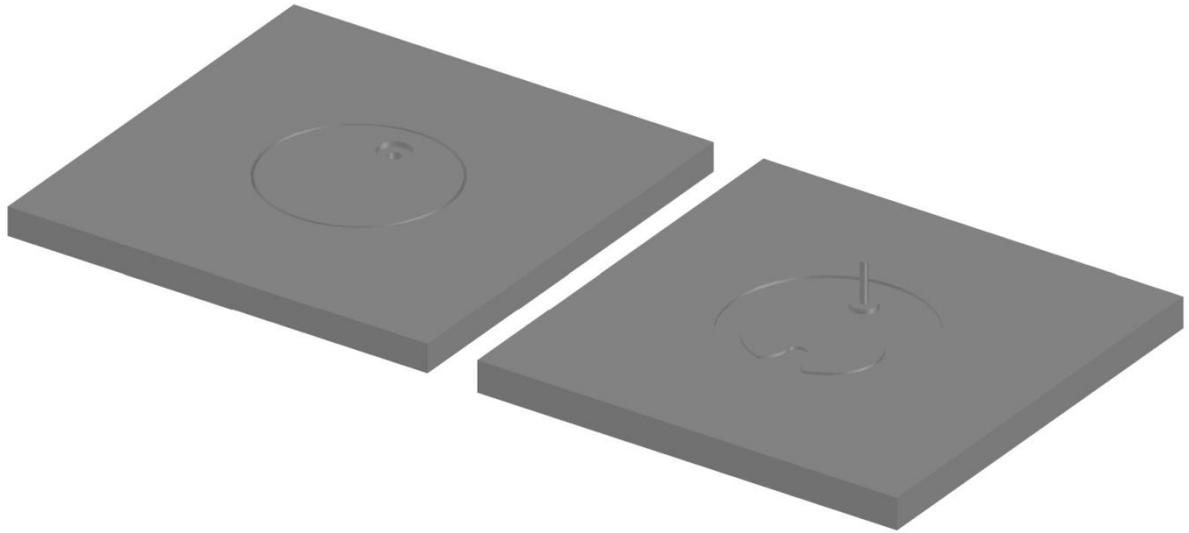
Molde para la pieza 1.2 tapa pequeña.
